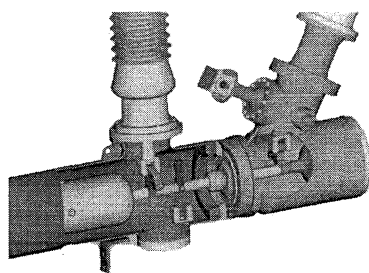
Двойной комбинированный разъединитель-заземлитель для применения с двойной системой шин (на рисунке оба разъединителя показаны подключенными к различным сборным шинам)
